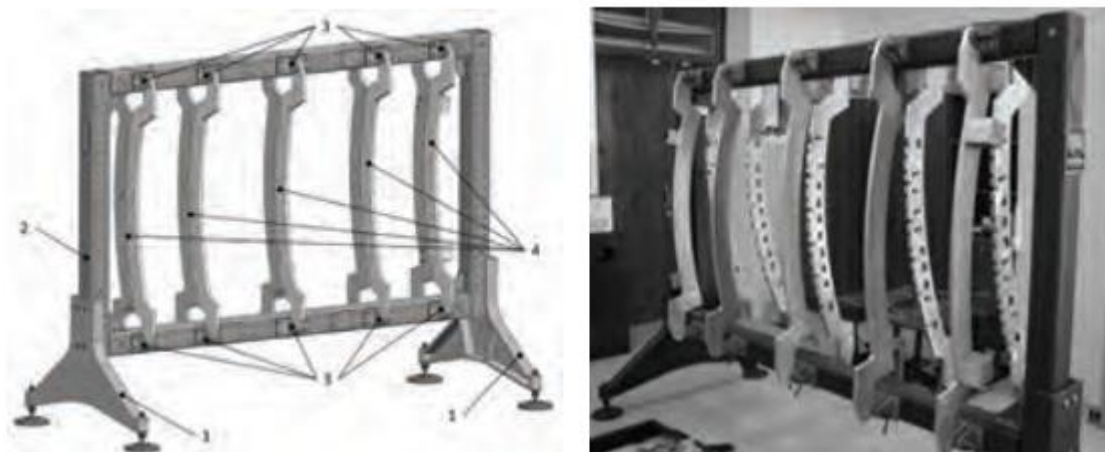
Схема комплекса автоматизированного монтажа сборочного приспособления
